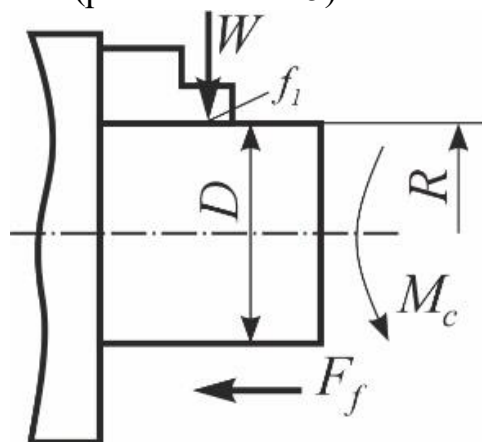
Эскиз для расчета силы зажима W заготовки, закрепленной в 3-кулачковом токарном патроне
